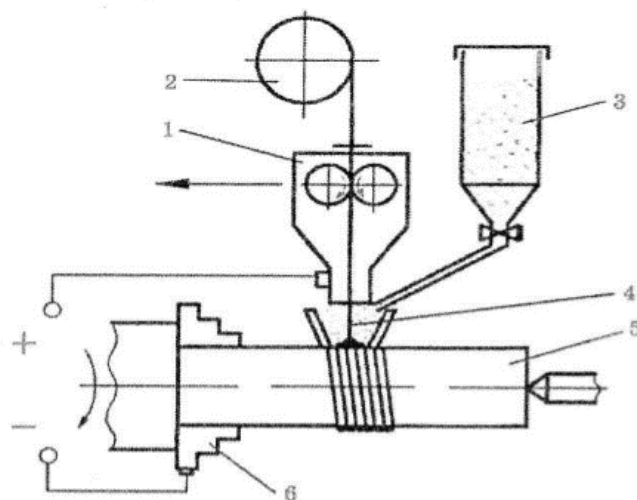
Принципова схема електродугового наплавлення деталей під флюсом: 1 – наплавляюча голівка; 2 – касета з електродним дротом; 3 – бункер з флюсом; 4 – електродний дріт; 5 – відновлювана деталь; 6 – патрон токарного верстату
